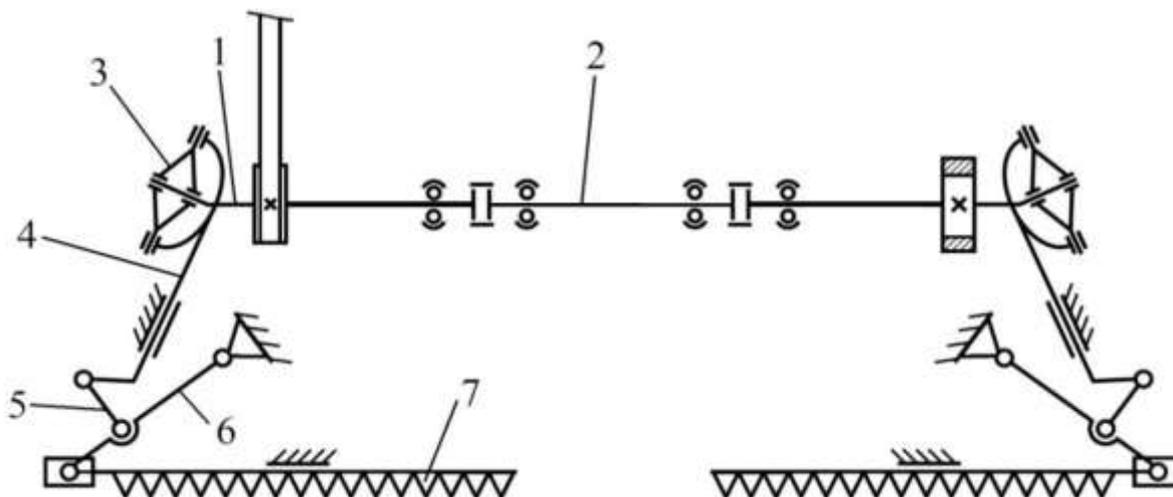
Схема привода с механизмами «качающаяся шайба»
